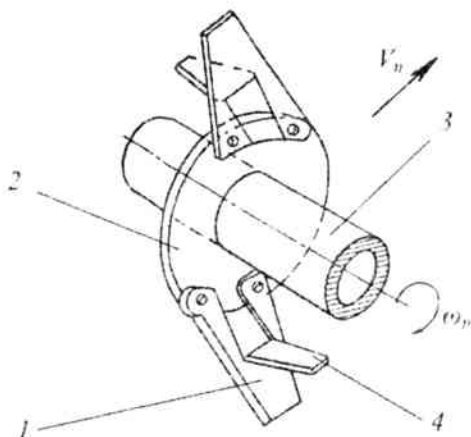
Ротационный рабочий орган для послойной обработки почвы, снабженный ножами с вырезными окнами: 1 – основной прямой нож; 2 – диски; 3 – вал ротора; 4 – дополнительный боковой нож
